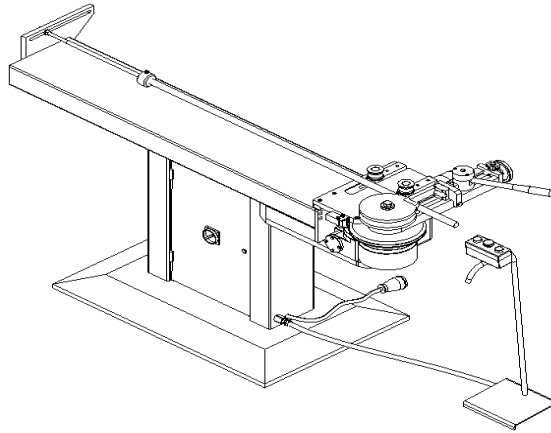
CNC Kontrol Boru- Profil Bükme Makinası
